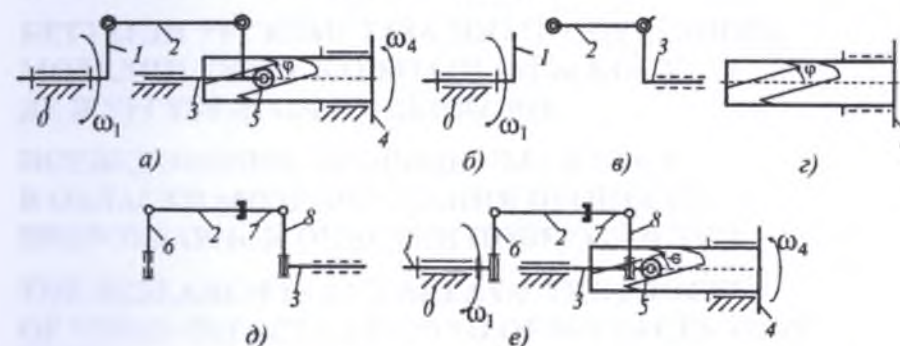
Пространственные рычажные редукторы: 0 – стойка; 1 – кривошип; 2 шатун; 3 – ведомый кривошип; 4 – ползун; 5 – ролик; 6 и 7 – стержни; 8 – толкатель
